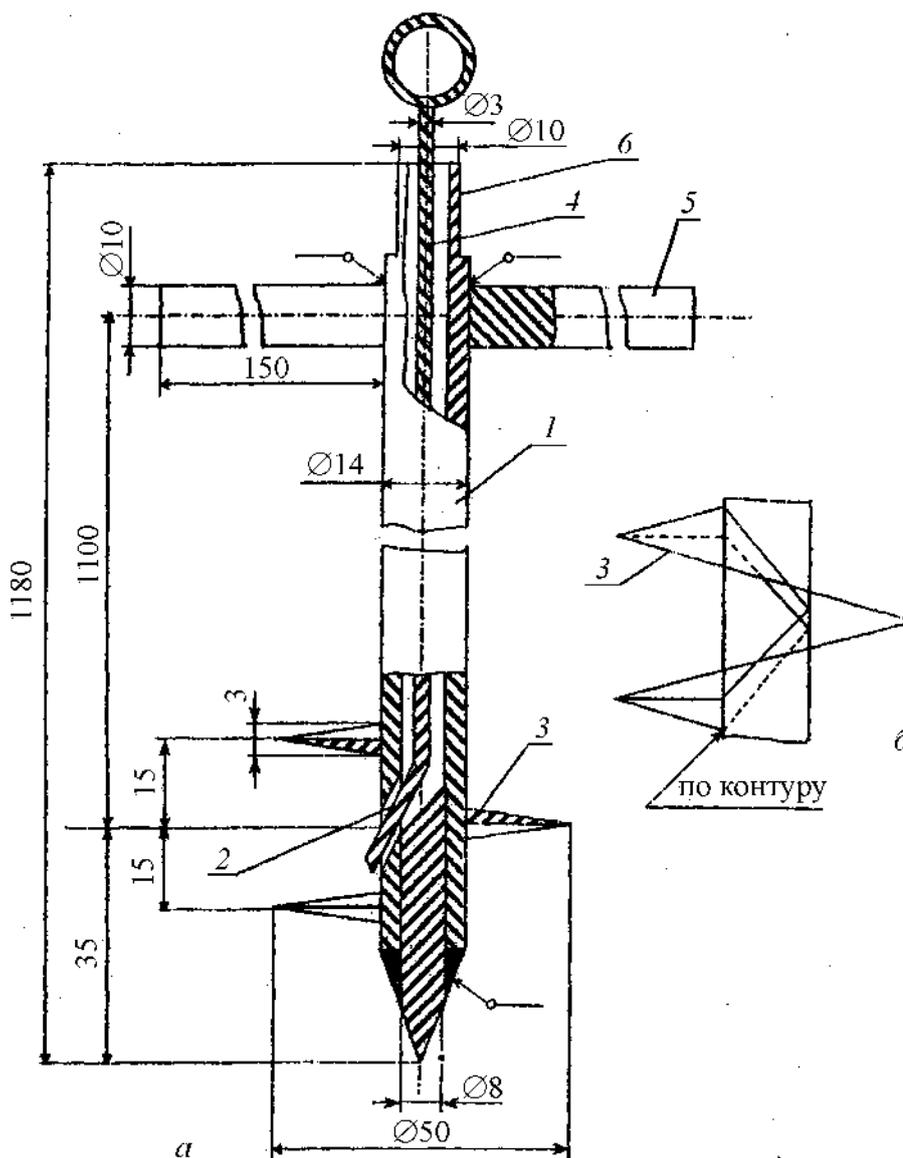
Воздухоотборное устройство (а) и шнековая навивка (б): 1 – стальная труба; 2 – газосборное отверстие; 3 – отрезок шнековой навивки; 4 – запирающий элемент; 5 – ручки для погружения устройства в грунт; б – газозаборный штуцер
